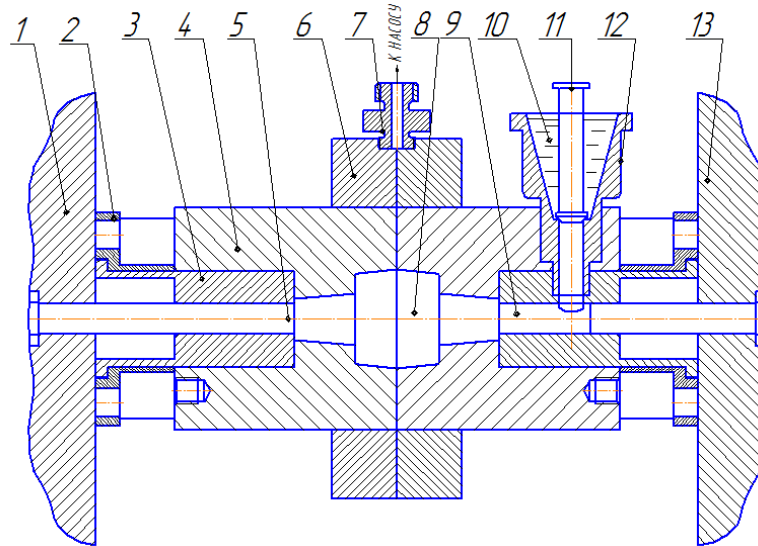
Схема процесса: 1 - левая подвижная плита; 2 - левый упор; 3 - левая камера прессования; 4 - левая полуформа; 5 - левый прессующий плунжер; 6 - бандаж; 7 - штуцер для связи с вакуумным насосом; 8 - полость формы; 9 - правый прессующий плунжер; 10 - жидкий металл; 11 - стопор; 12 - заливочная чаша; 13 - правая неподвижная плита
